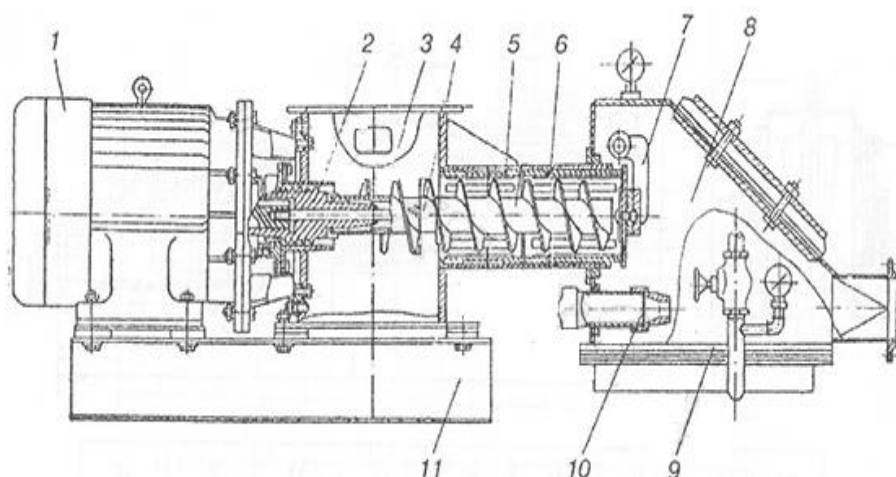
Пневмовинтовой насос ТА-14Б: 1 — электродвигатель; 2 — уплотнение; 3 — корпус; 4 — шнек; 5,6 — гильза; 7 — обратный клапан; 8 — смесительная камера; 9 — аэроднище; 10 — сопло; 11 — рама
